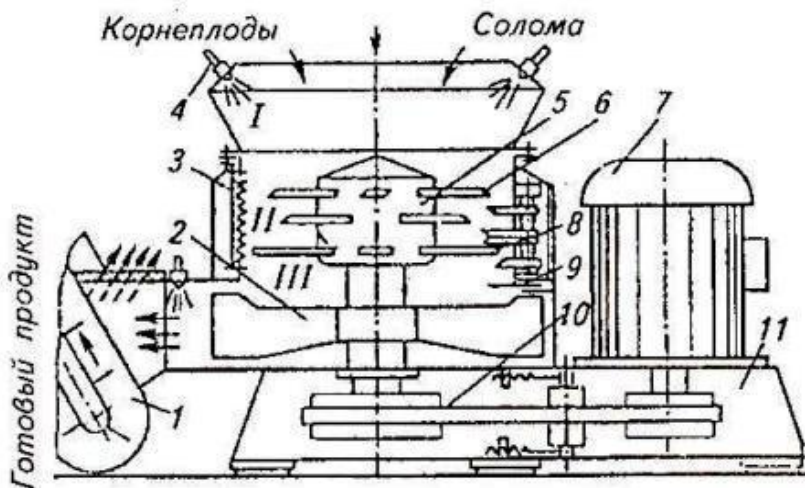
Схема измельчителя-смесителя ИСК-3: 1 – выгрузной транспортёр; 2 – швырялка; 3 – дека; 4 – форсунка; 5 – ротор; 6 – молотилки; 7 – электродвигатель; 8 – ножи; 9 – шибер; 10 – привод ротора; I – приёмная камера; II – рабочая камера; III – выгрузная камера
